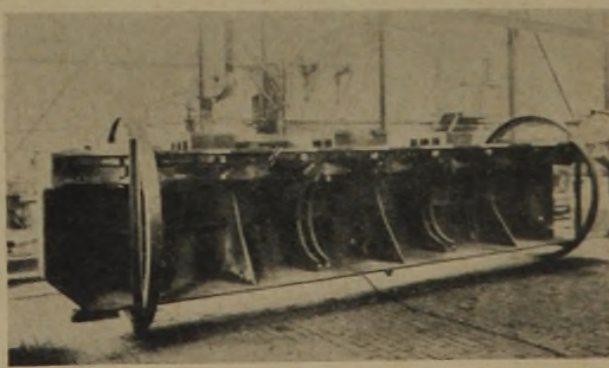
Arbeitsrollgang einer Blockstraße in geschweißter Ausführung
